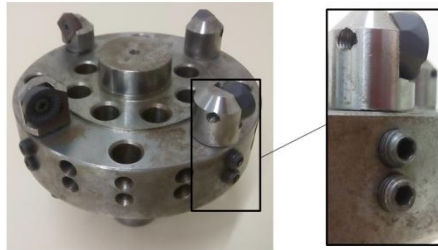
Торцева касетна фреза (D=125 мм) з двома затискними гвинтами
